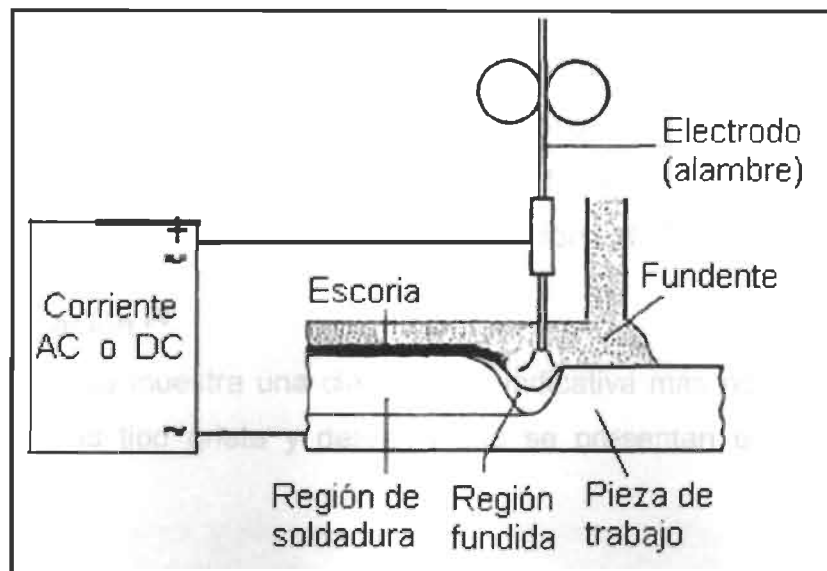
Esquema del proceso de soldadura por arco sumergido.^[1]
